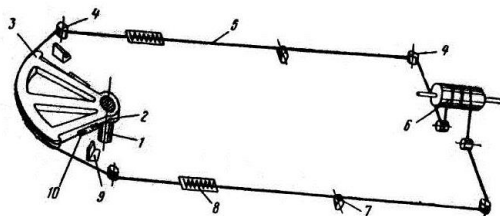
Секторный привод со штуртросовой передачей. 1 – баллер руля; 2 – крепление штуртроса; 3 – сектор; 4, 7 – блоки; 5 – штуртрос; 6 – барабан; 8 – буферные пружины; 9 – ограничительный башмак; 10 – талреп винтовой
